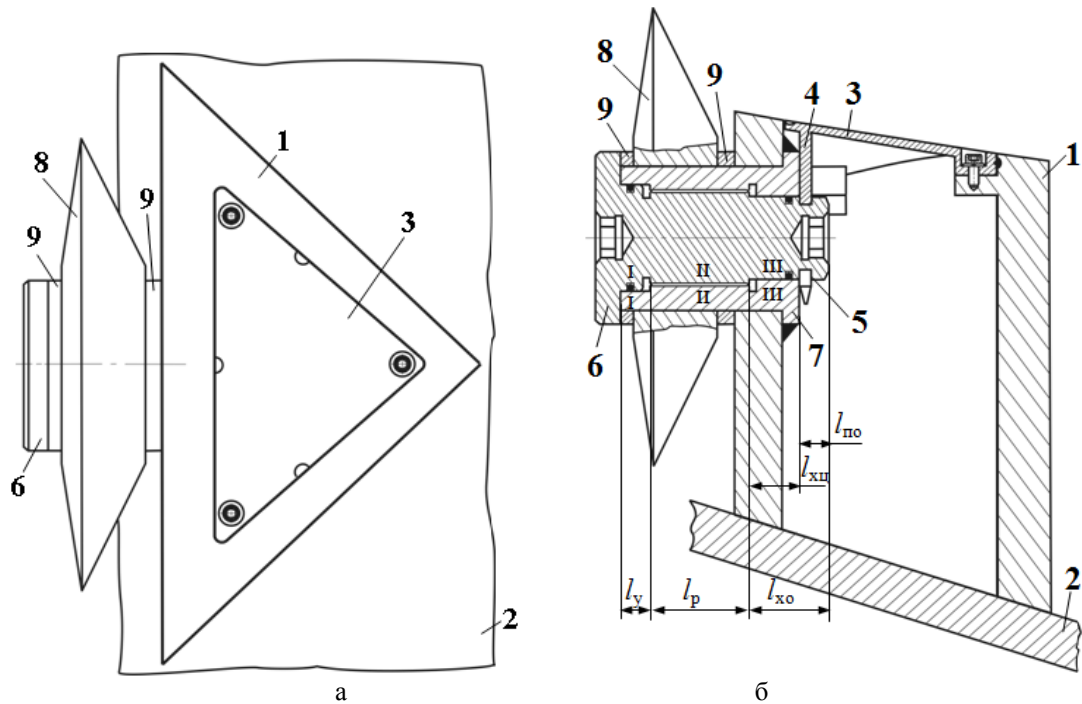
Устройство трехгранной призмы с узлом крепления дискового инструмента:
